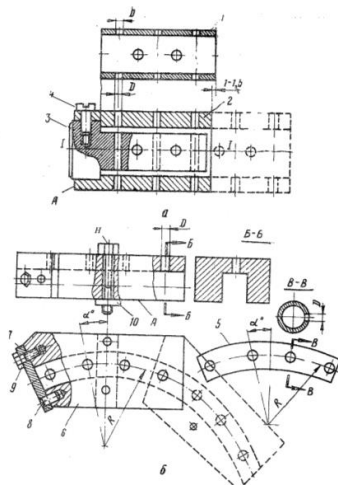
Схемы сверления отверстий с применением шагающего кондуктора в коротких и длинных трубках: а – прямых; б – изогнутых по радиусу R
